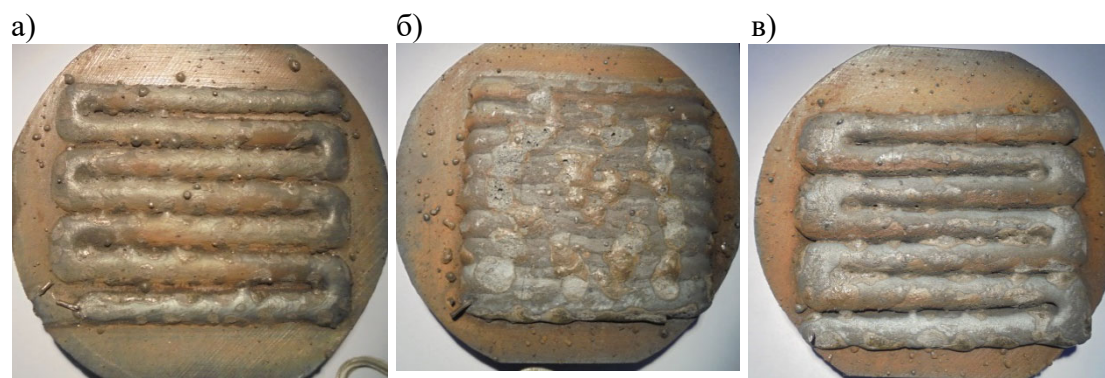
Образцы с высокотвёрдыми наплавками: а – с разрядкой между слоями наплавки; б – сплошная наплавка; в – с двойной по высоте наплавкой
